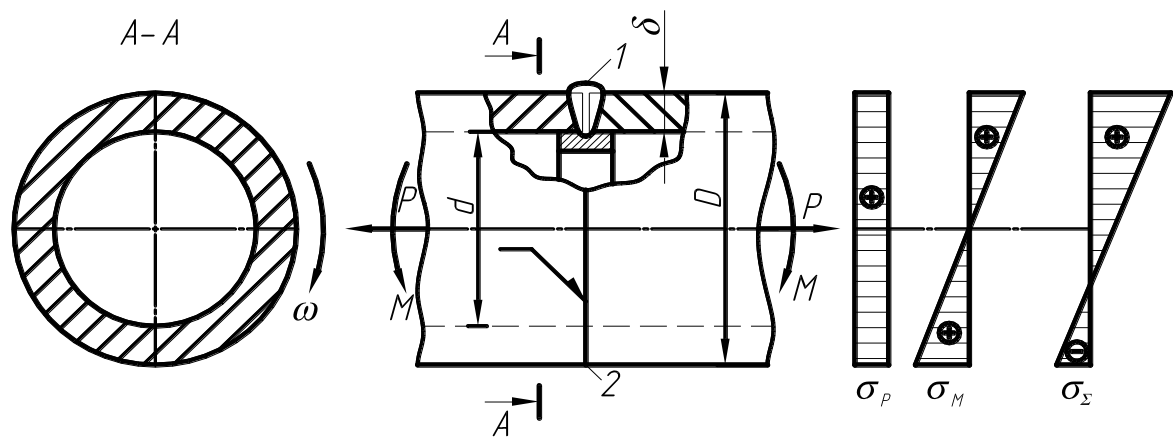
Сварка трубчатого вала встык на плотной подкладке
